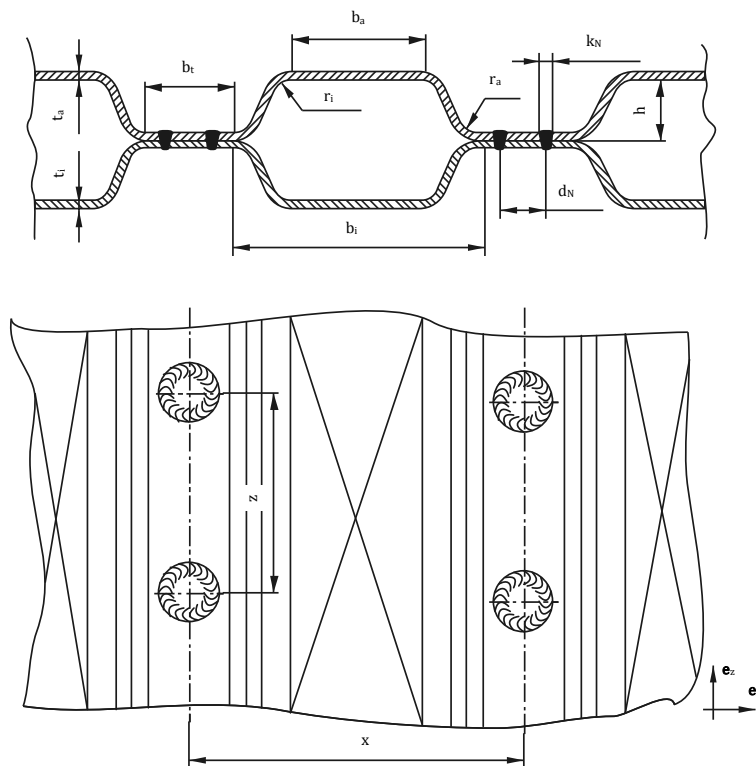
Geometrieskizze „Beidseitiges Trapezblech direktverschweißt“
